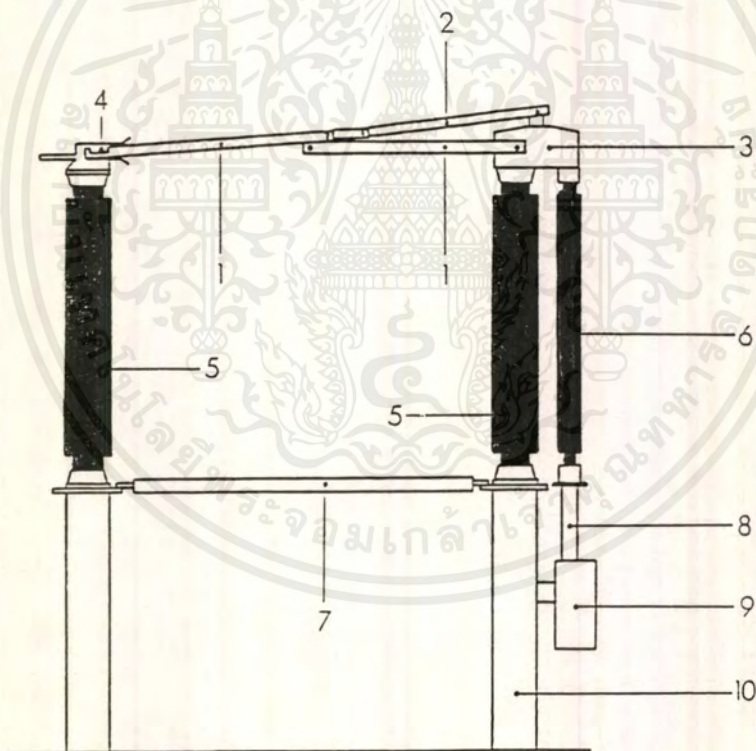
โครงสร้าง Horizontal centre-break Disconnecting switch
